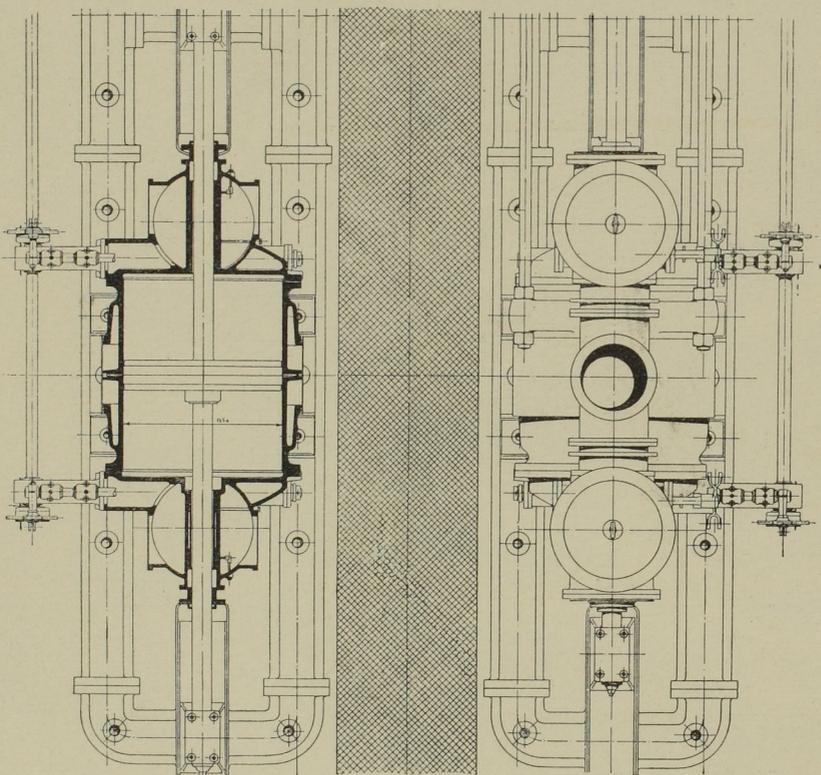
Grundriss und Längsschnitt des Windzylinders. Massst. 1 : 60.
